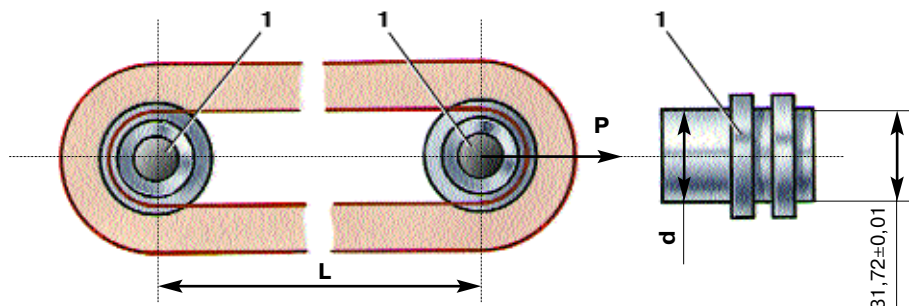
Схема проверки износа (вытяжки) цепи двигателя мод. 2106–70: 1 – ролики
